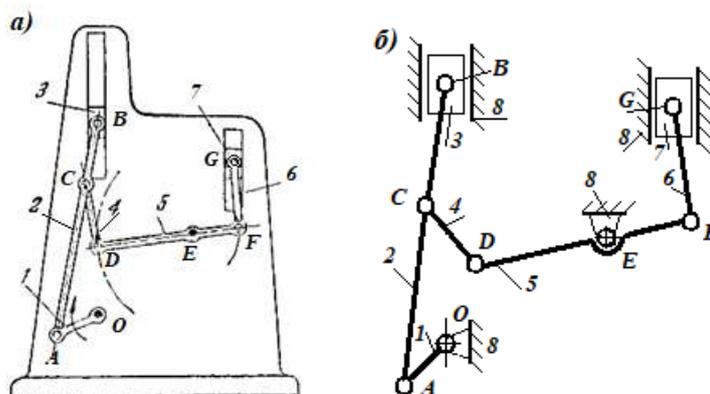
Восьмизвенный рычажный механизм: а – полуконструктивная схема; б - кинематическая схема
